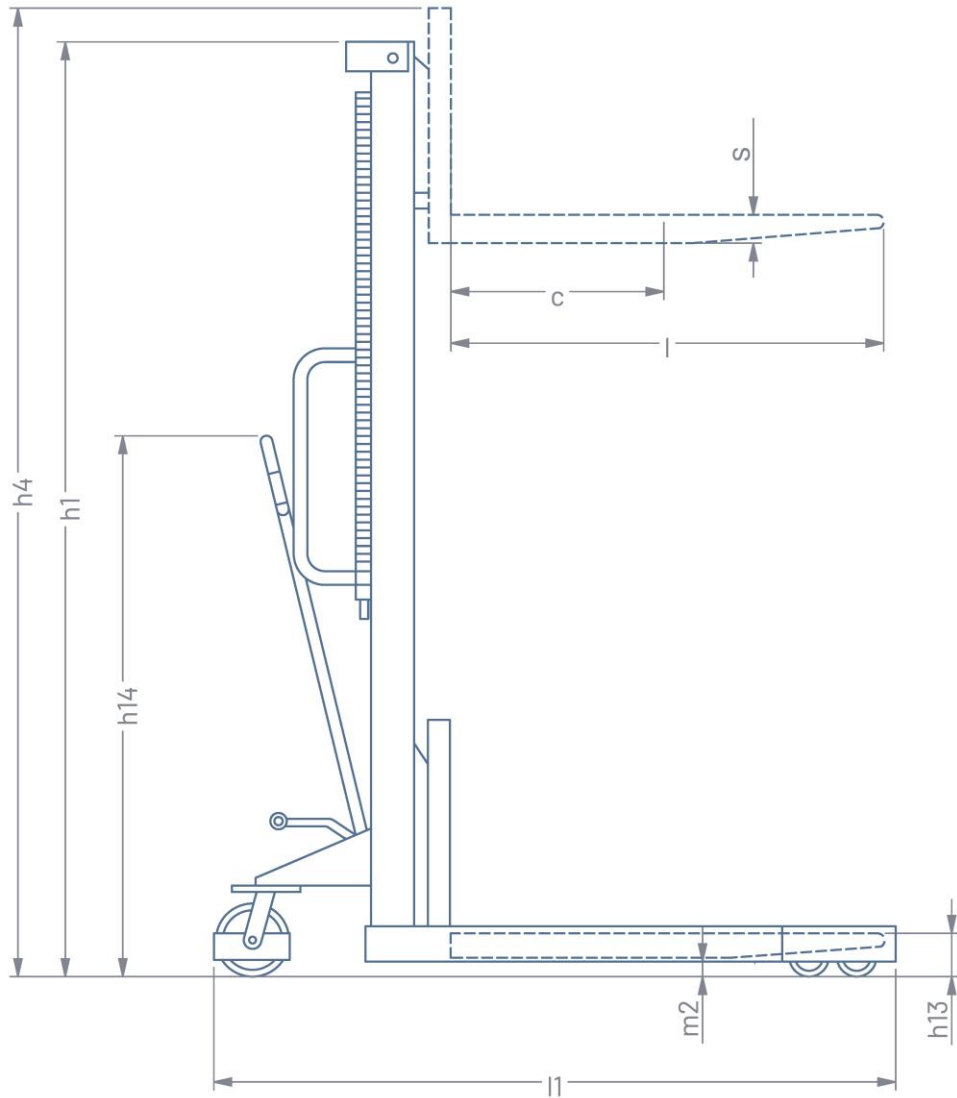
Seitenansicht des WIDE mit Kürzeln
